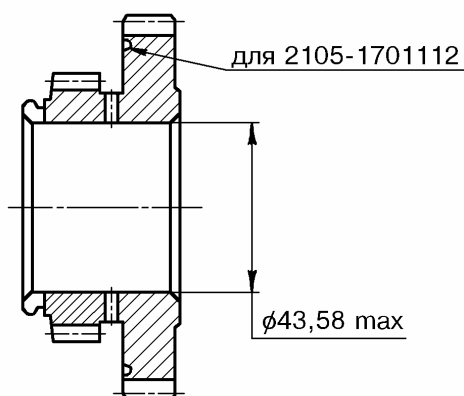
Шестерни вторичного вала – 2101-1701112, 2101-1701127, 2101-1701131, 2105-1701112.
